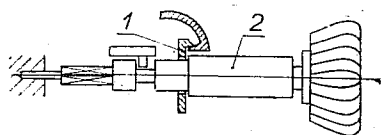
Stopień odchylenia się wieczka odskokowego.
